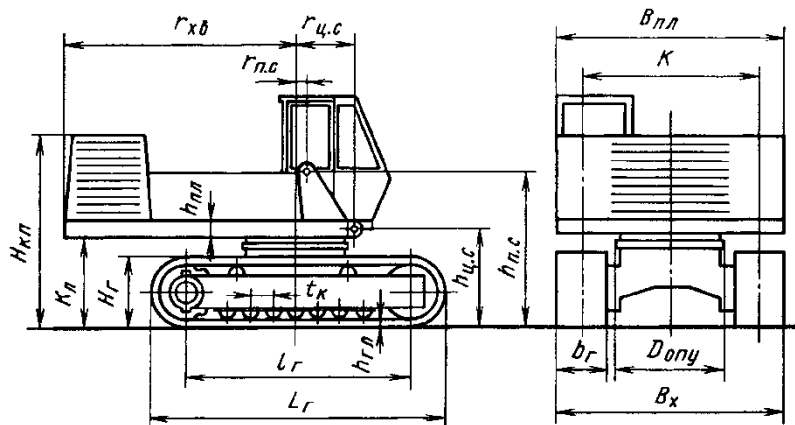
Схема основных размеров базовой части одноковшового экскаватора
